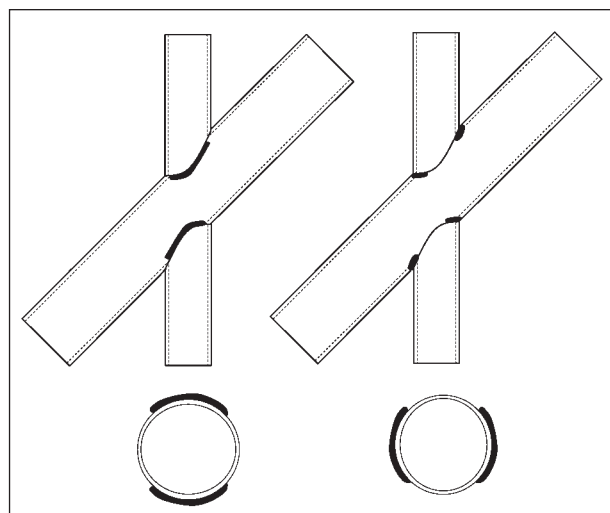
Empfohlene modifizierte Schweißnahtausbildung der Prüfstücke
